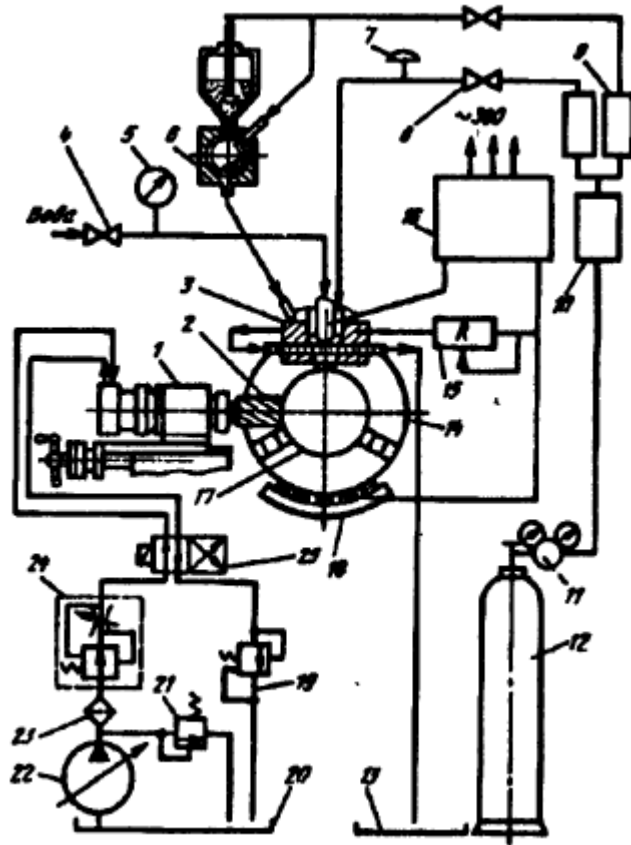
Схема установки для ППМО: 1 – фрезерна головка; 2 – фреза; 3 – плазмотрон; 4, 8 – вентилі; 5 – манометр; 6 – дозатор; 7 – реле; 9 – ротаметр; 10 – ресивер; 11 – редуктор; 12 – балон з газом; 13 – гідробак; 14 – патрон; 15 – резистор; 16 – джерело живлення; 17 – заготовка; 18 – струмознімач; 19 – пропорційний клапан; 20 – мастильний бак; 21 – запобіжний клапан; 22 – гідронасос; 23 – фільтр; 24 – регулятор гідронасосу; 25 – регулятор потоку.
